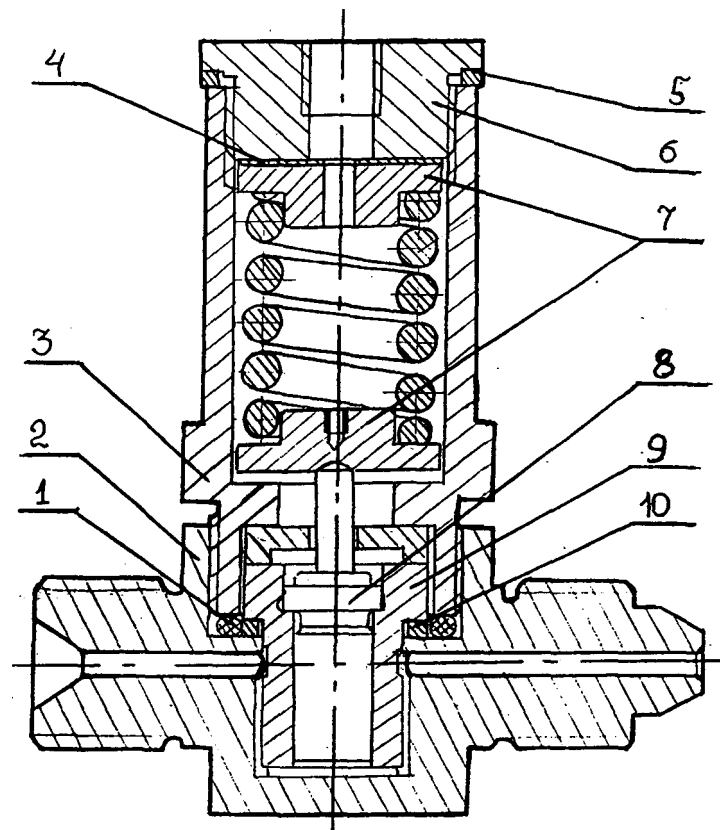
Конструкция унифицированного опытно-промышленного образца МИД для ТА тепловозных дизелей различного типа: 1, 5, 10- уплотнительные кольца; 2- корпус; 3- стакан; 4- регулировочная прокладка; 6- нажимной штуцер; 7- тарелка пружины; 8- поршень; 9- втулка.
